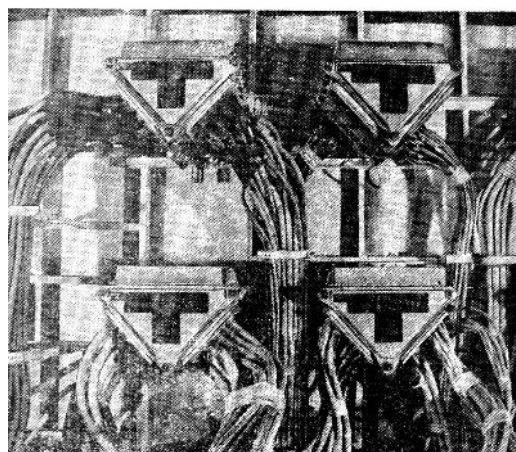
Установка кабельных соединителей СКС на переборке блок-модуля
